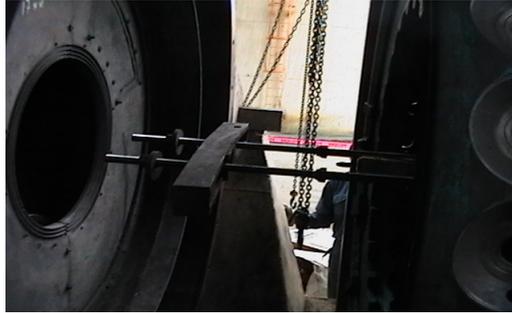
Montaje del conjunto de rodamientos en las guías
